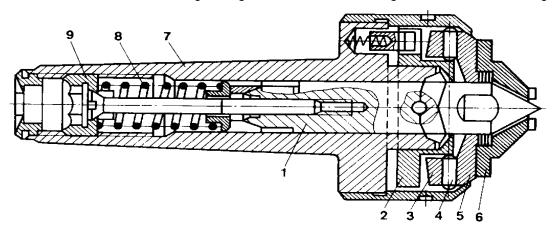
Поводковый зубчатый патрон со сменными поводками: 1 – плавающий центр; 2 – стакан; 3 – люлька; 4 – ролик; 5 – водило; 6 – самоустанавливающийся поводок; 7 – корпус; 8 – пружина; 9 – гайка
